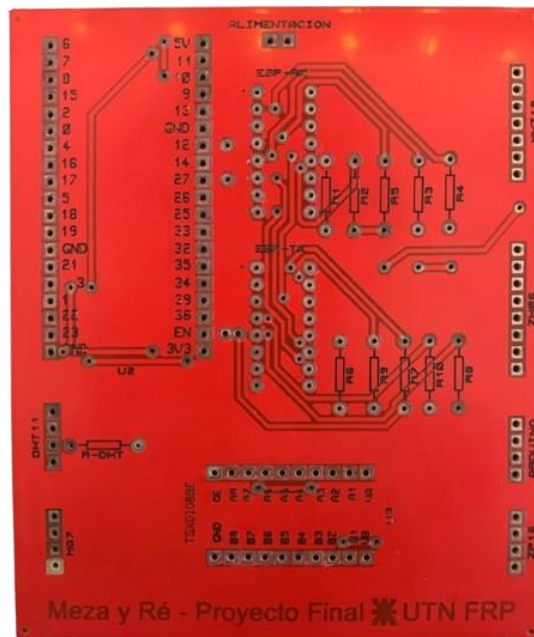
Diseño PCB – Placa impresa [fuente propia]
